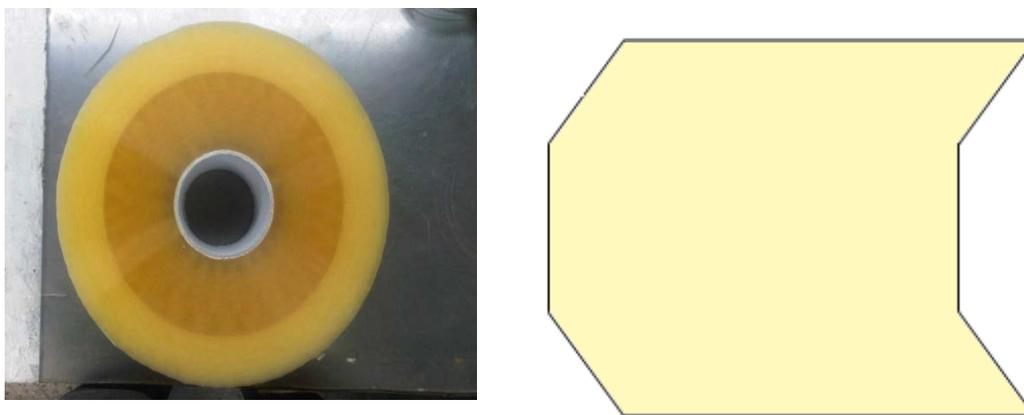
Log Roll telescopiado visto desde planta y desde perfil.
